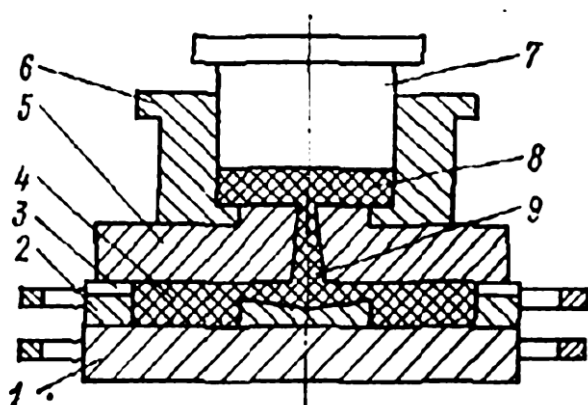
Съемная пресс-форма для литьевого прессования с верхней загрузочной камерой: 1 – нижняя плита; 2 – матрица; 3 – воздушные каналы; 4 – изделие; 5 – верхняя плита; 6 – загрузочная камера; 7 – шток; 8 – пресс-остаток; 9 – литниковые каналы
